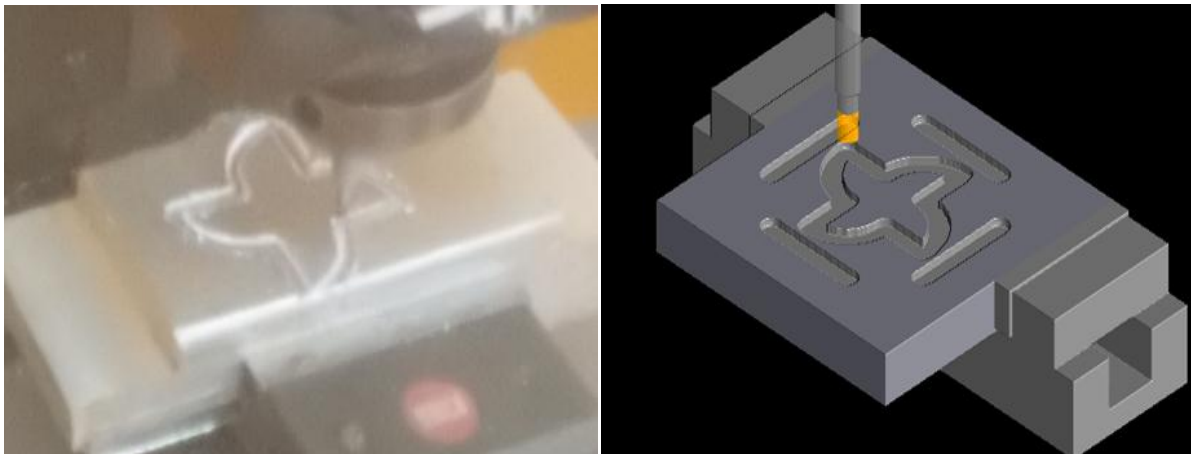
la pièce réalisée par la machine et simulée par WinCTS
